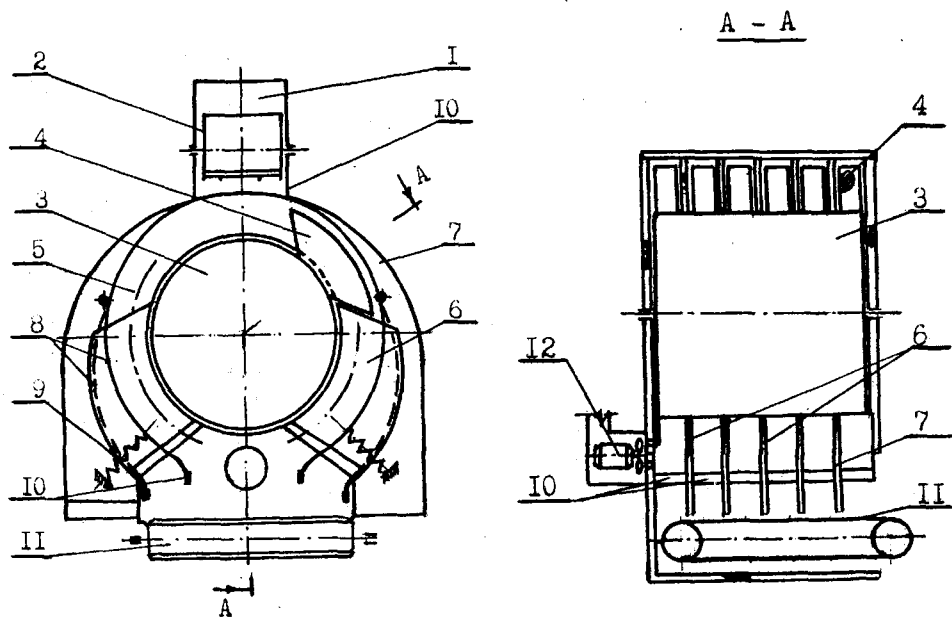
Технологическая схема установки с криволинейной рабочей камерой и поворотным уплотнителем.
